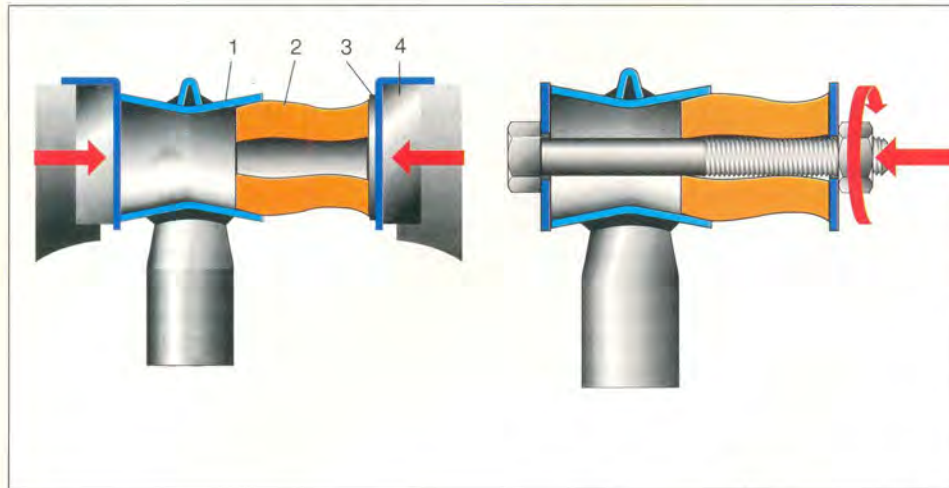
Установка в проушину резиновой втулки: а – в тисках; б – с помощью болта; 1 – проушина; 2 – втулка; 3 – шайба; 4 – тиски.
